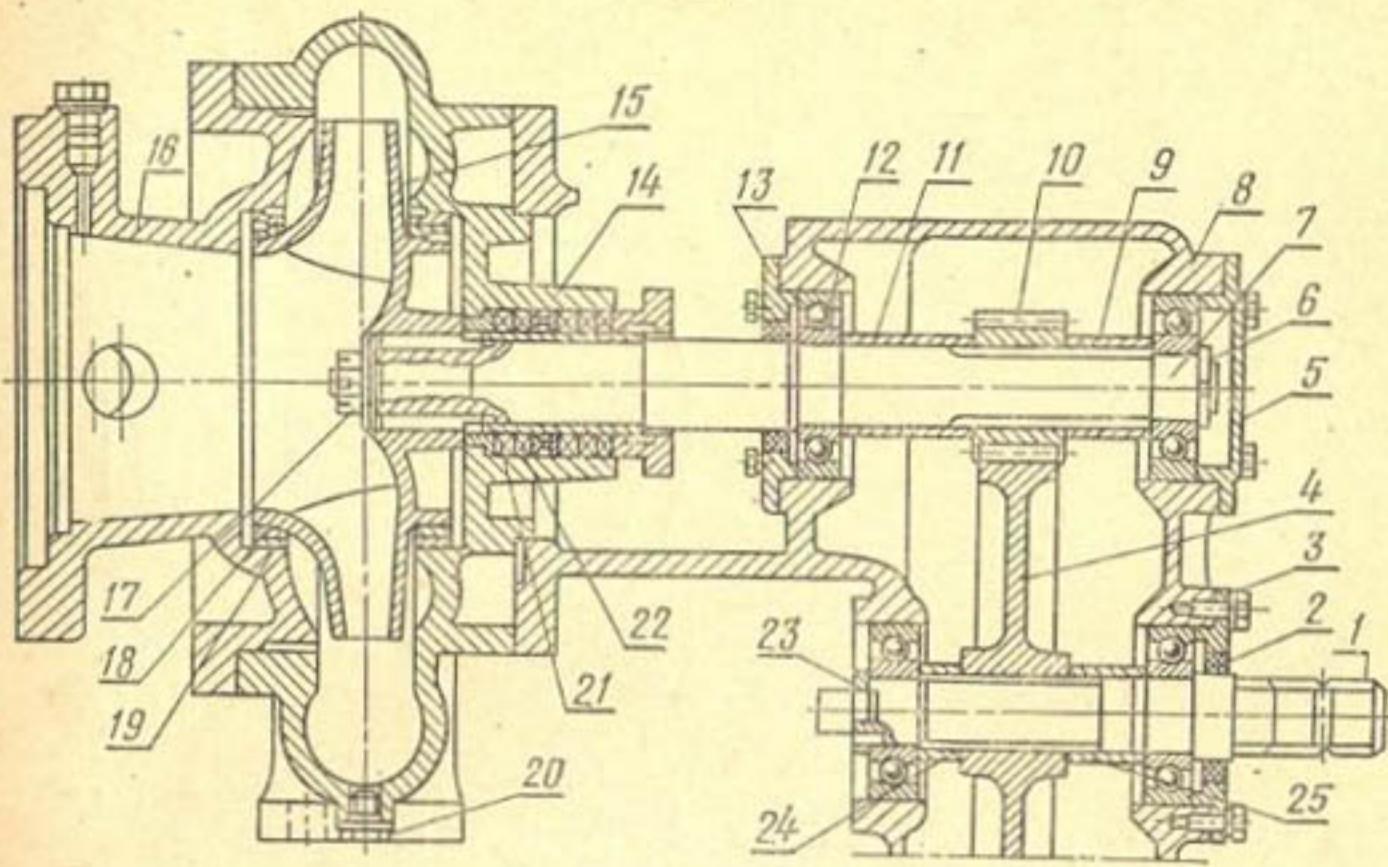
Насос-редуктор дождевателя ДДН-70:
